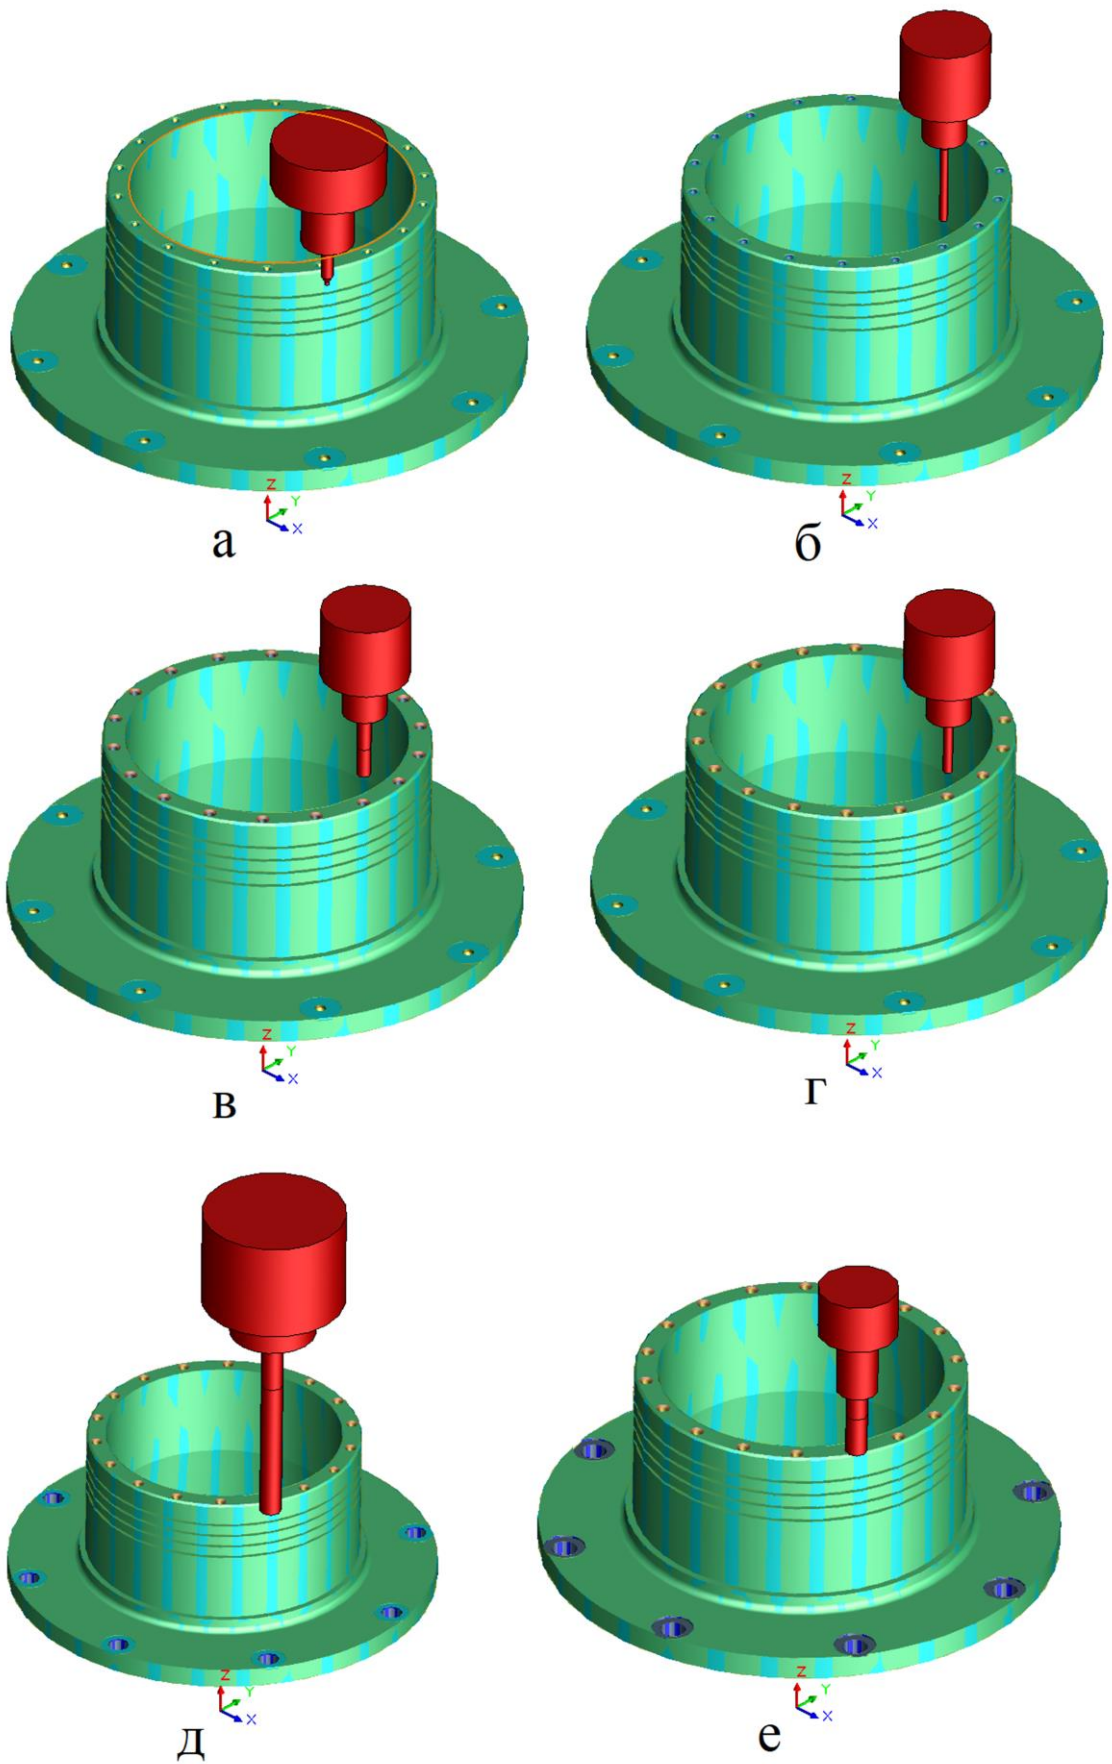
Фрагменти імітації процесу обробки деталі: а – при центруванні отворів; б – при свердлінні; в – при зенкуванні; г – при нарізанні різьби; д – при свердлінні; е – при фрезеруванні;
